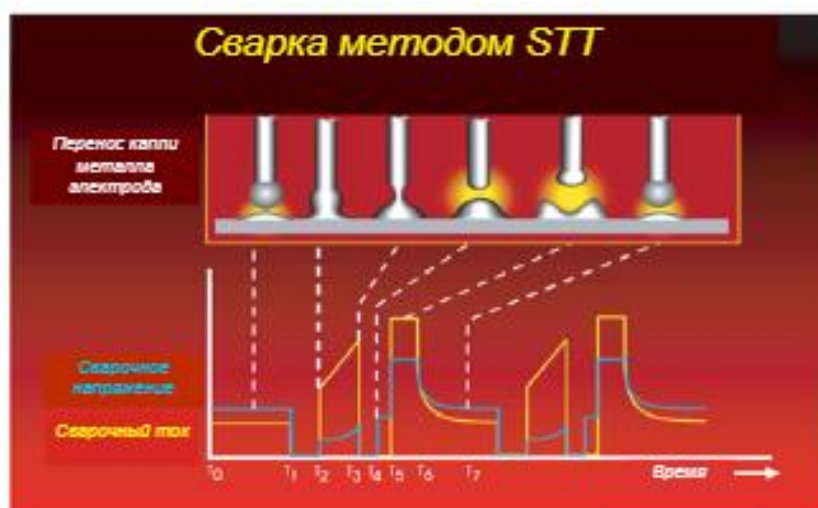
Формы кривых сварочного тока и напряжения при полуавтоматической сварке STT
